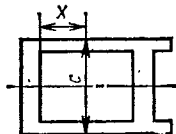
Размеры, охватывающие полые профили из алюминиевых и магниевых сплавов
